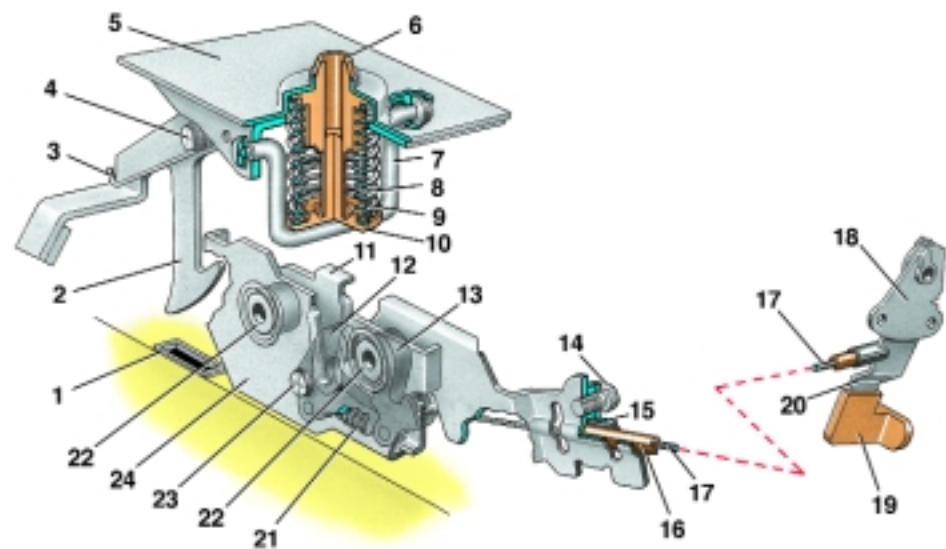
Защелка замка капота, предохранительный крючок, замок капота и его привод: 1 – вставка предохранительного крючка; 2 – предохранительный крючок; 3 – пружина предохранительного крючка; 4 – ось предохранительного крючка; 5 – опорная пластина; 6 – держатель защелки; 7 – защелка; 8 – внутренняя пружина защелки; 9 – наружная пружина защелки; 10 – держатель пружин защелки; 11 – крышка корпуса замка; 12 – вилка замка; 13 – фиксатор вилки; 14 – болт держателя оболочки тяги привода замка; 15 – планка держателя; 16 – оболочка тяги; 17 – тяга привода замка; 18 – кронштейн рукоятки привода замка; 19 – наконечник рукоятки; 20 – рукоятка; 21 – пружина замка; 22 – резьбовая втулка; 23 – ось вилки замка; 24 – корпус замка
